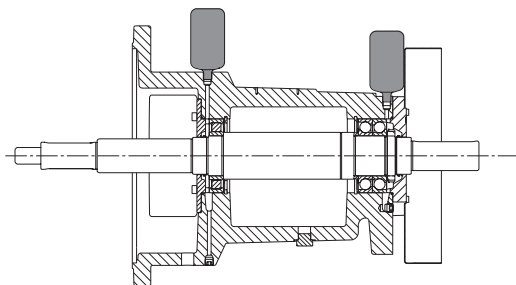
Корпус подшипников с открытыми роликовыми и двойными радиально-упорными подшипниками, смазываемыми автоматическими маслёнками для консистентной смазки
